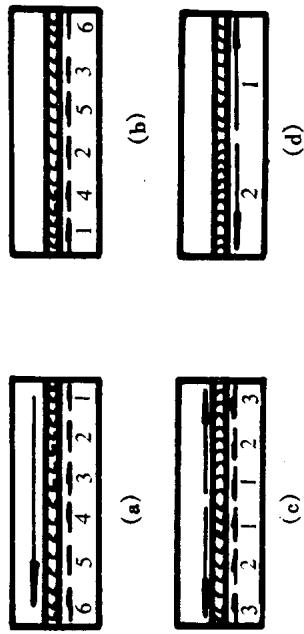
7 长焊缝分段焊的几种不同的焊接顺序
